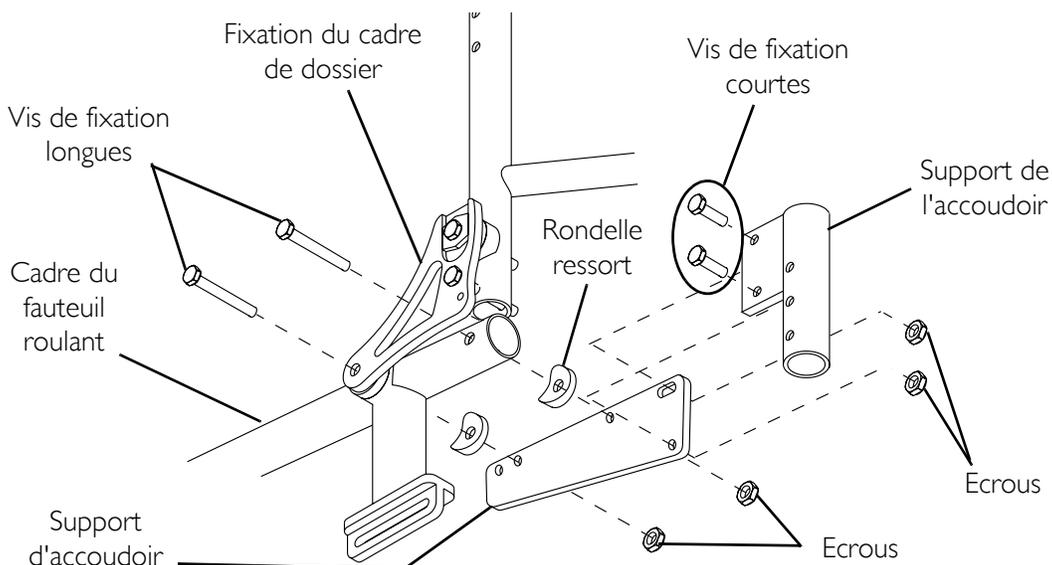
Installer l'ensemble de l'accoudoir tube rembourré escamotable
